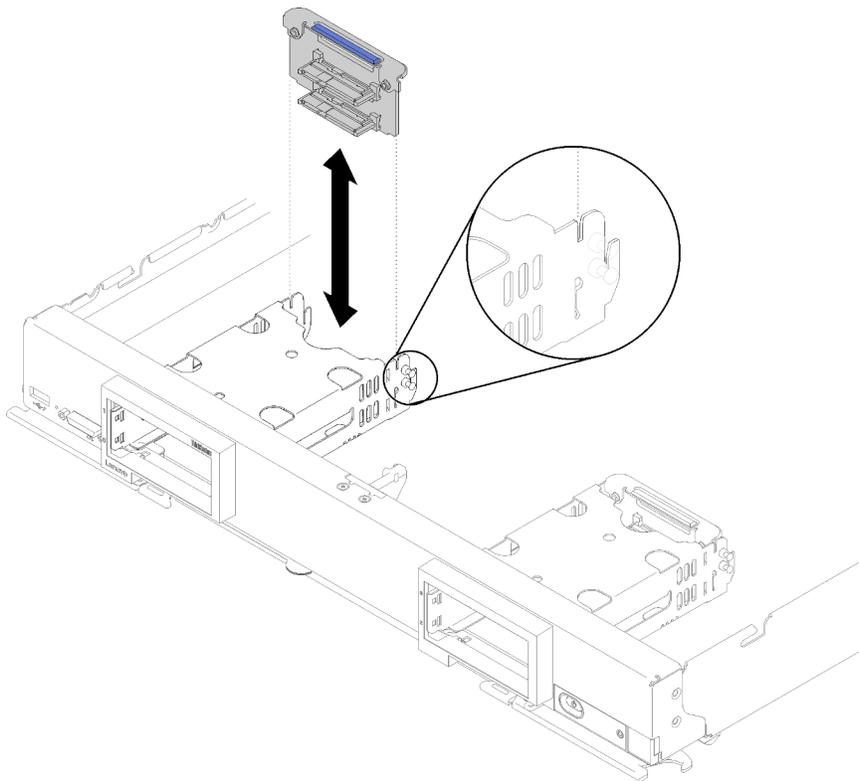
Entfernen der Rückwandplatte für 2,5-Zoll-Laufwerke
